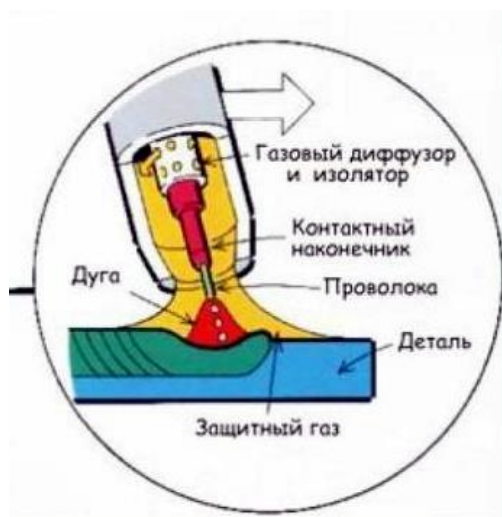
Схема выполнения механизированной сварки в защитных газах проволокой сплошного сечения
